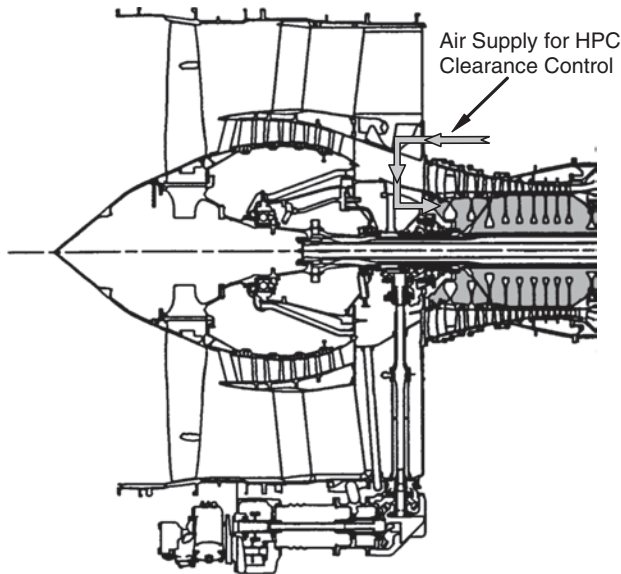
Prinzip der HPC Clearance Control. (© CFM)
